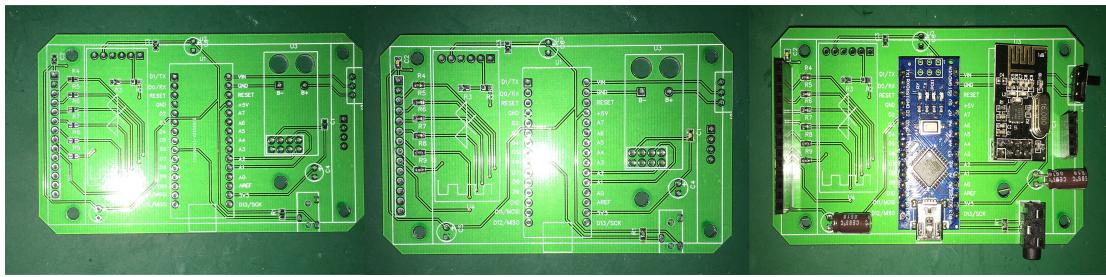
Circuito Impreso Antes y Despues de soldar sus componentes
